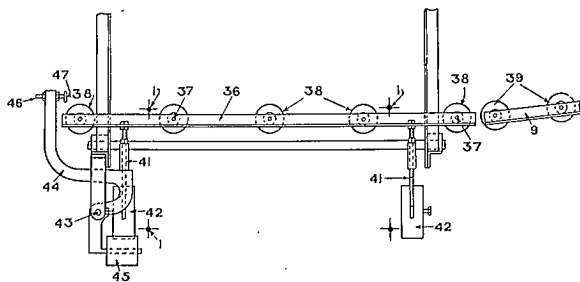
Plan du transporteur à rouleaux, système Persson.
